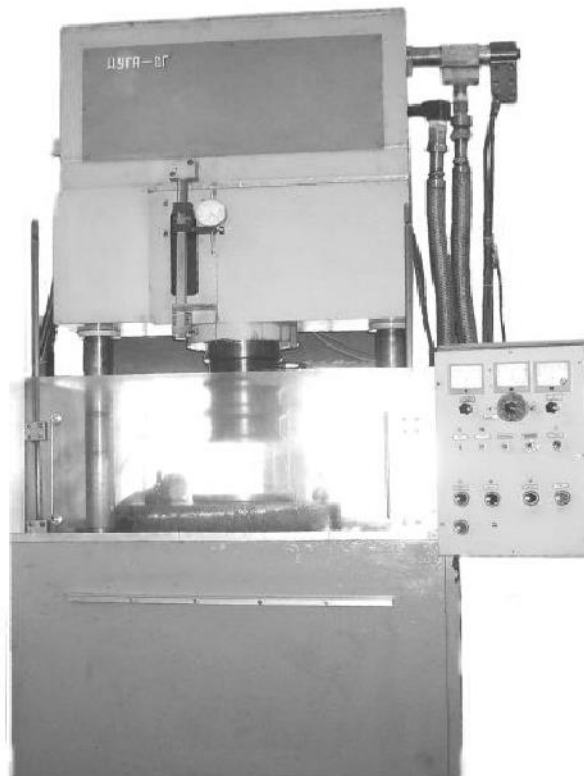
Універсальний копіювально-прошивний верстат "Дуга-8Г"
